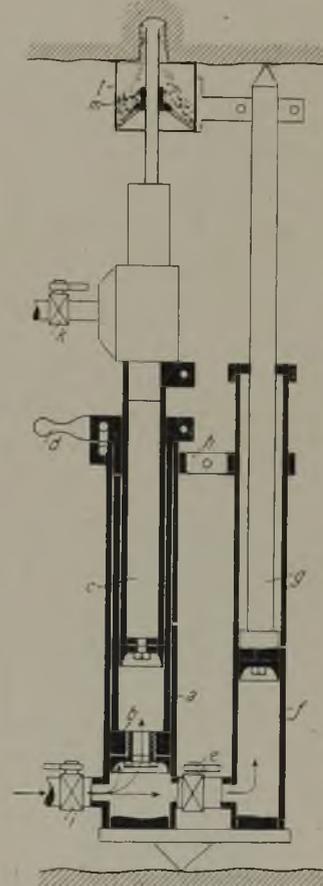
Aufbruchsäule der Bohrmaschinenfabrik Glückauf.
